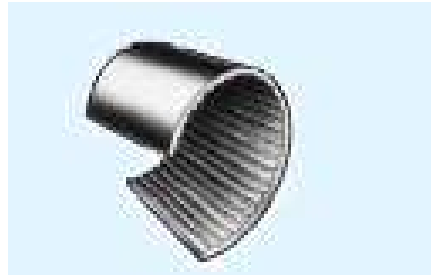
Стружка, формируемая режущими кромками фрезы с переменной схемой резания
